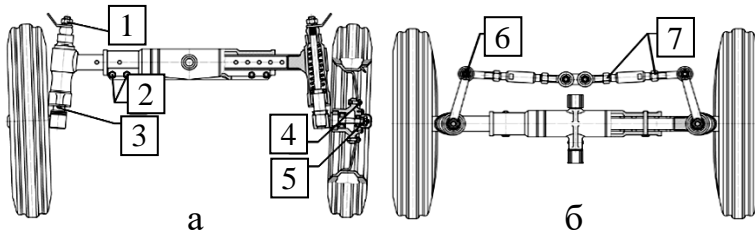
Схема керованого моста: а – вид спереду; б – вид зверху; 1...7 – точки розрегулювання
